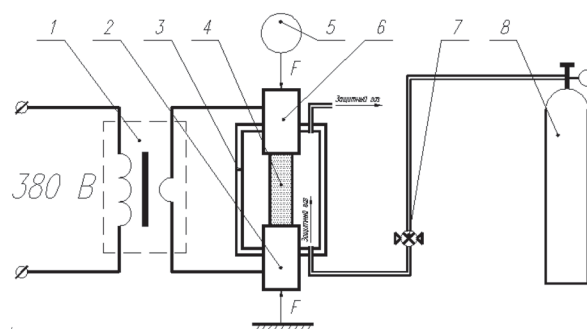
Схема устройства ЭКН пористых образцов: 1 – понижающий трансформатор; 2 – электрод нижний; 3 – камера с защитной атмосферой; 4 – обрабатываемый образец; 5 – устройство нагружения; 6 – электрод верхний; 7 – редуктор; 8 – баллон с аргоном
